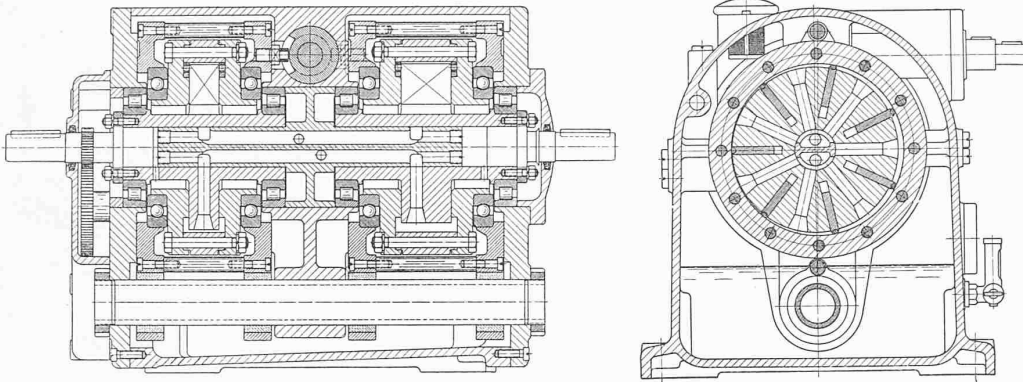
Universal-Sturm-Pressölgetriebe der Werkzeug- und Werkzeugmaschinenfabrik Albert Roller in Waiblingen.
